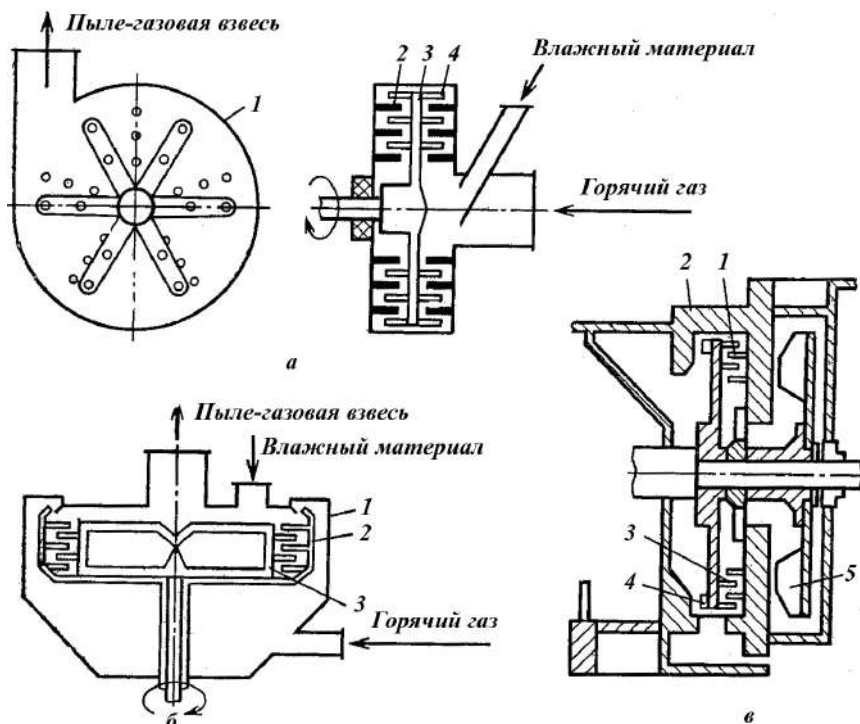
Конструкции измельчителей: а – ударная мельница; б – мельница с вертикальным ротором; в – молотково-штифтовая мельница; 1 – корпус; 2 – неподвижные штифты; 3 – крестовина с вращающимися штифтами; 4 – вентиляционные лопатки; 5 – молотки.
